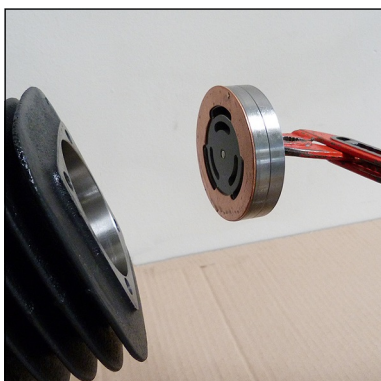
Neues Saug- / Druckventil in Zylinder ausgerichtet einsetzen
